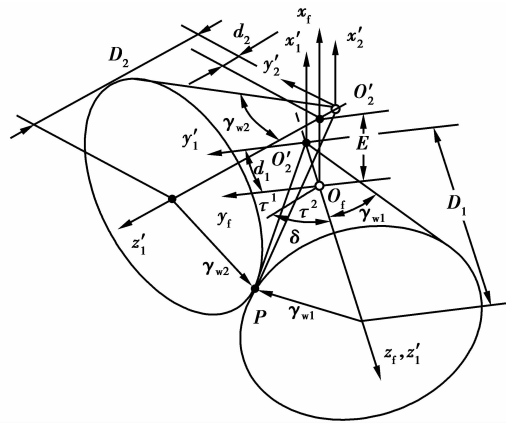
交错轴变厚齿轮工作节锥面及坐标变换
